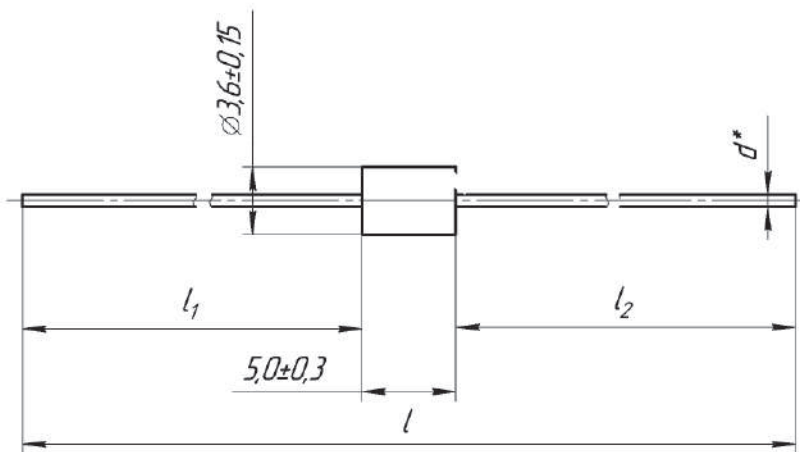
Габаритные размеры фильтров ФЭМИ-1-1, ФЭМИ-1-2
